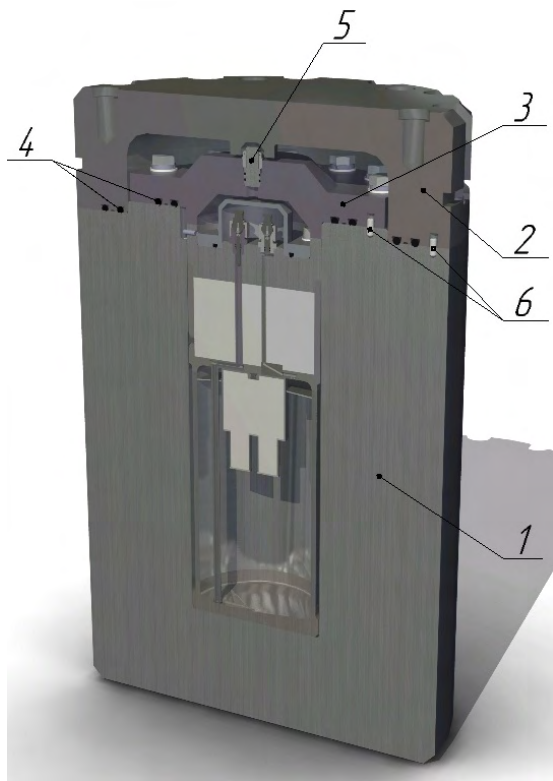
Контейнер: 1 – корпус; 2 – крышка наружная; 3 – крышка внутренняя; 4 – уплотнительные кольца; 5 – заглушка; 6 – штифты
